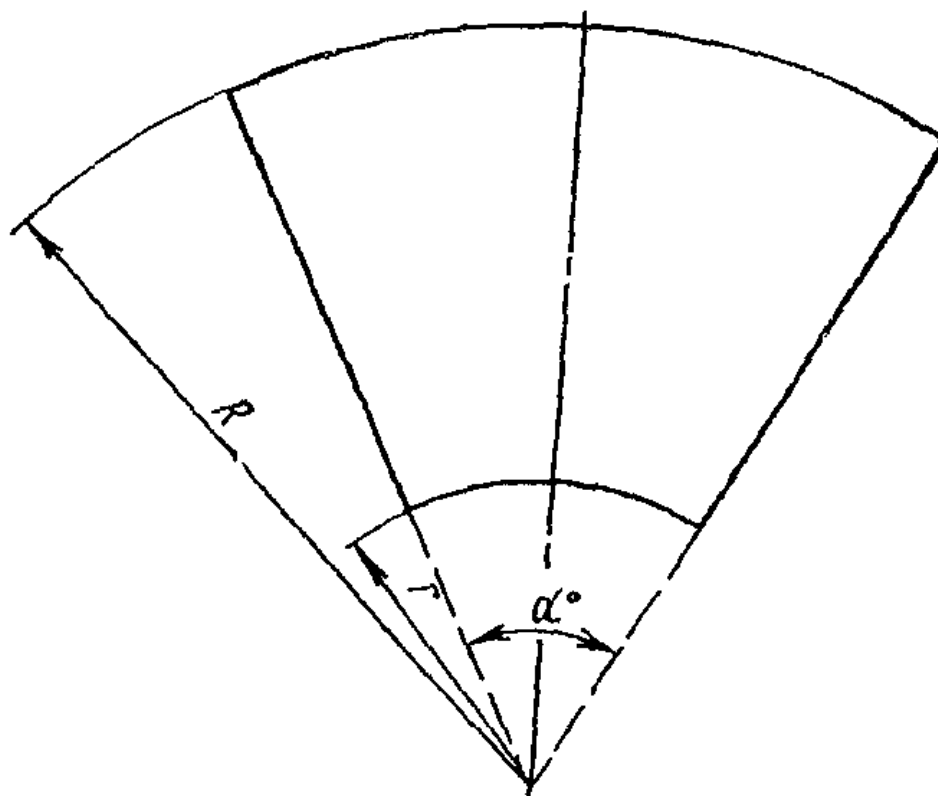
Раскрой формы для отливки корпуса концевой заделки типа ПКВэ
